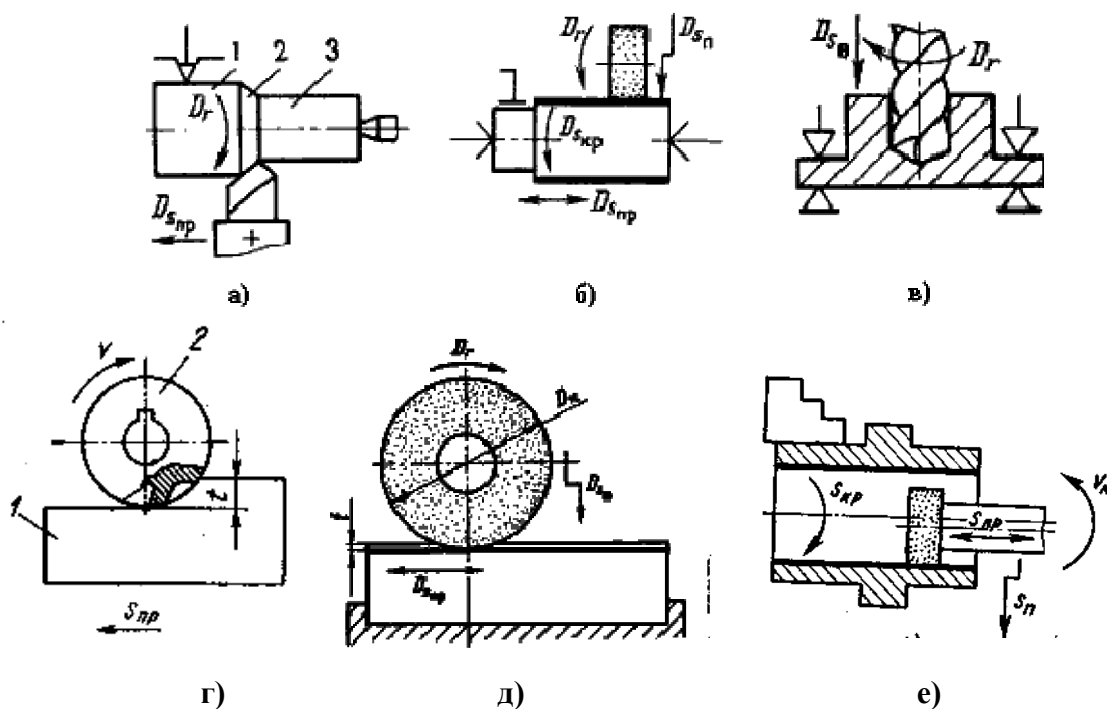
Схемы обработки заготовок: а – точением; б – шлифованием на круглошлифовальном станке; в – сверлением; г – фрезерованием; д – плоским шлифованием; е – внутренним шлифованием.
